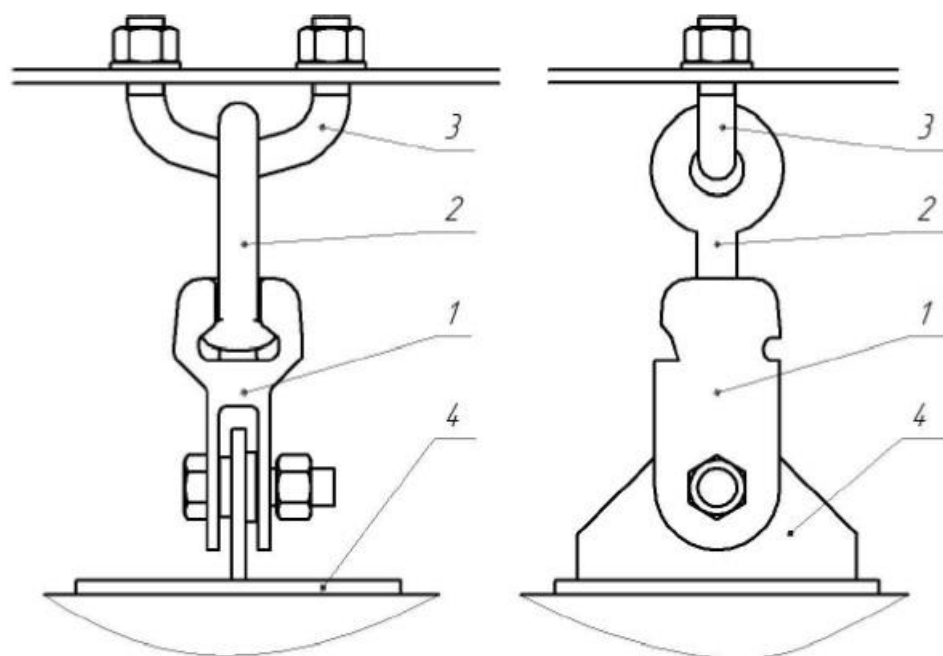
Крепление устройств I-TOR (E-TOR) на опоре высоковольтной ЛЭП:
